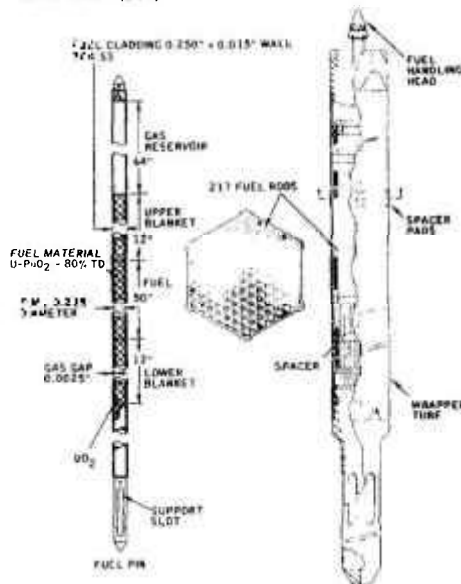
Elemento Combustível (Assembly) do LMFBR (USA)
